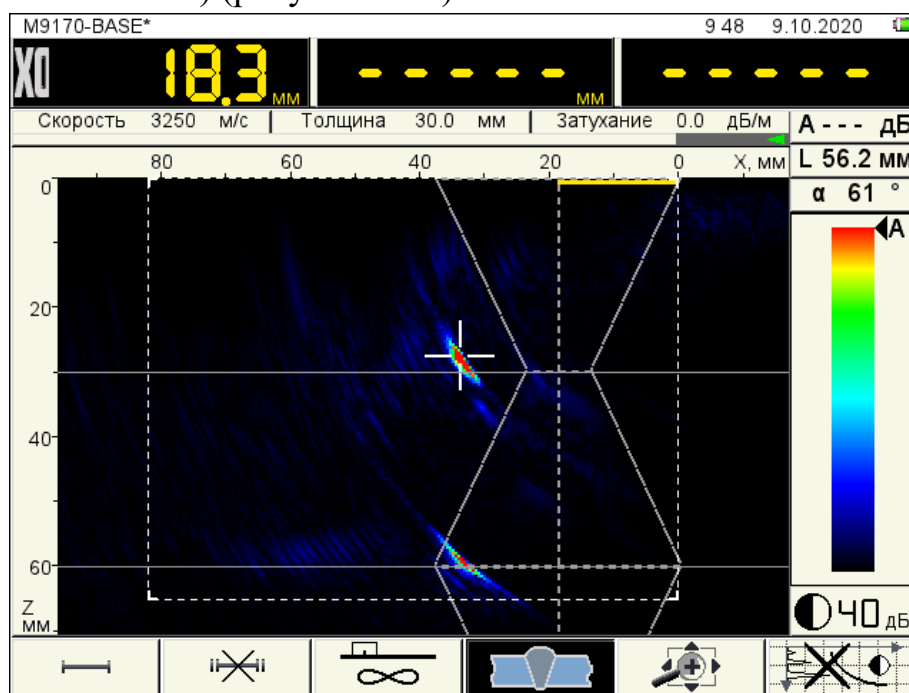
Вид экрана с маской сварного шва, установленной вплотную к антенной решётке
